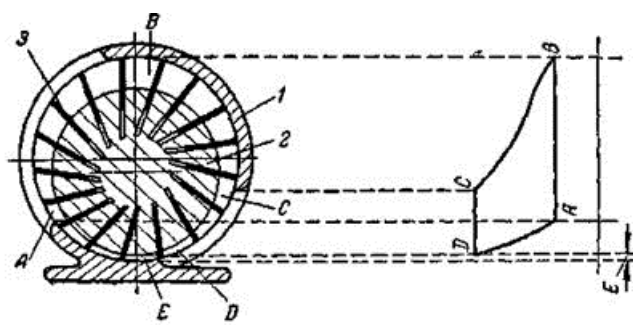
Схема ротационного пластинчатого компрессора:
